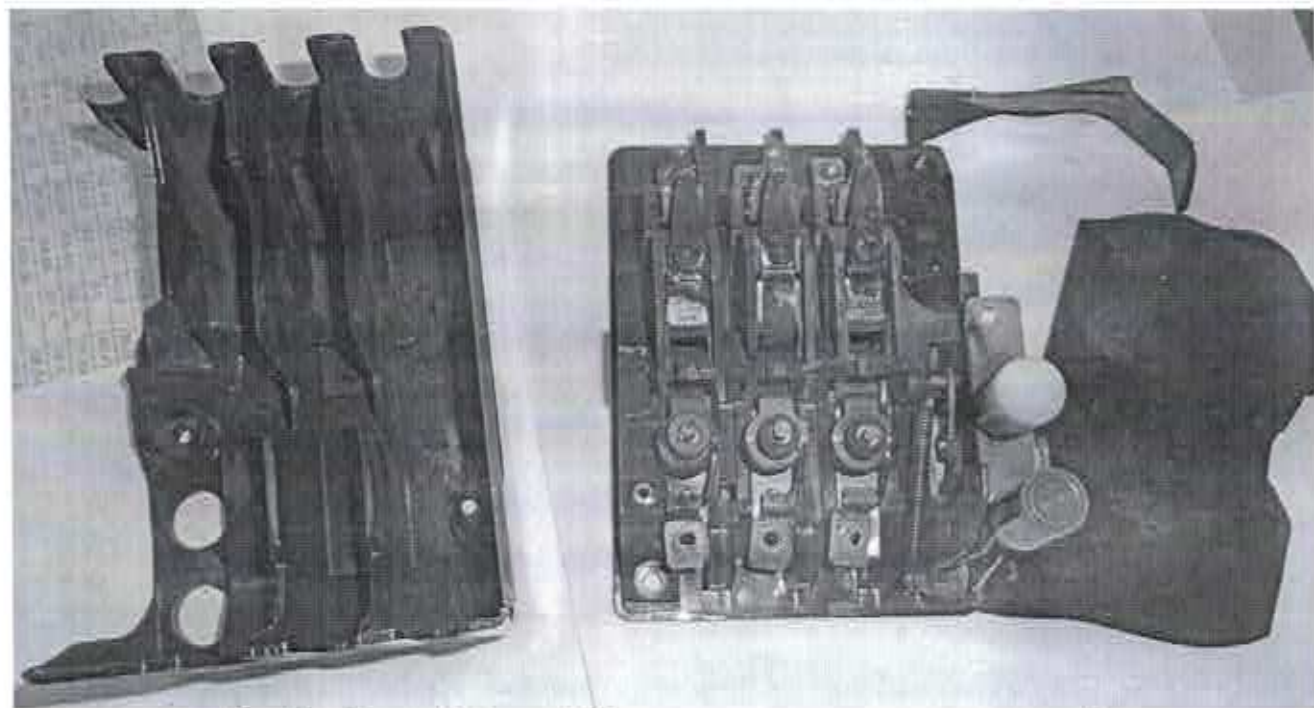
Образец № 9 после ПКС, крышка развалилась на несколько частей
